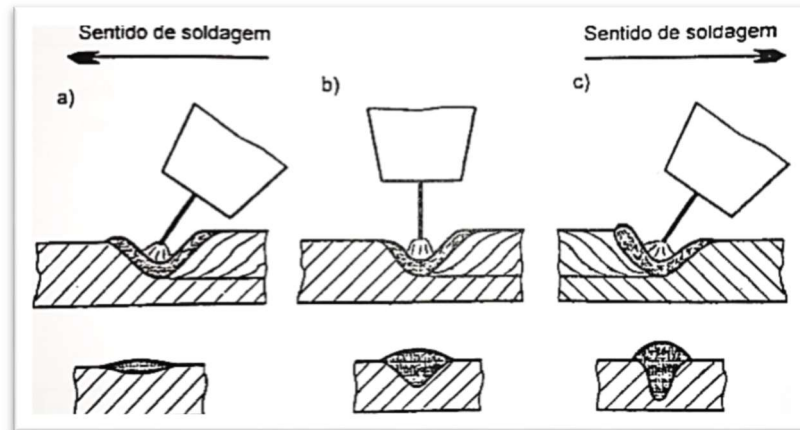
Inclinações aplicadas à soldagem MIG/MAG⁽²⁸⁾.
